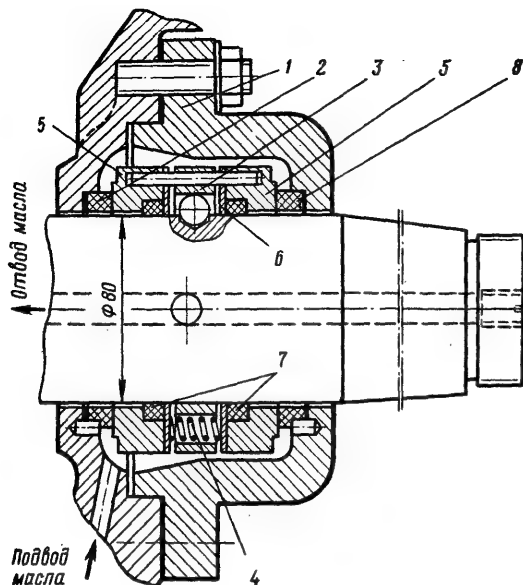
Сальник пружинный уплотнения конца вала (компрессор П80):
